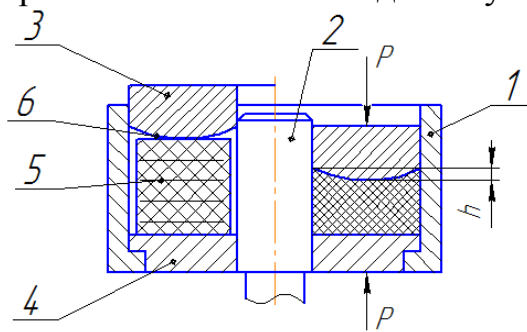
Пресс-форма с сегментной верхней формовочной плитой:
